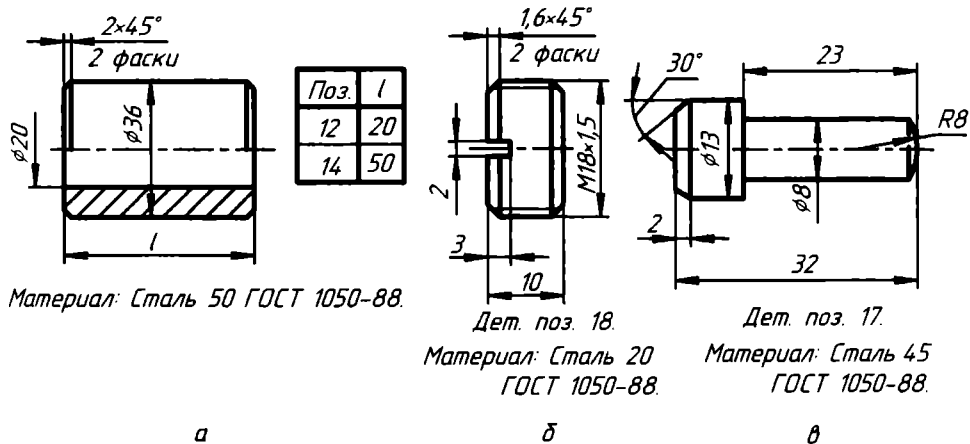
Чертежи: а — роликов; б — пробки; в — толкателя
